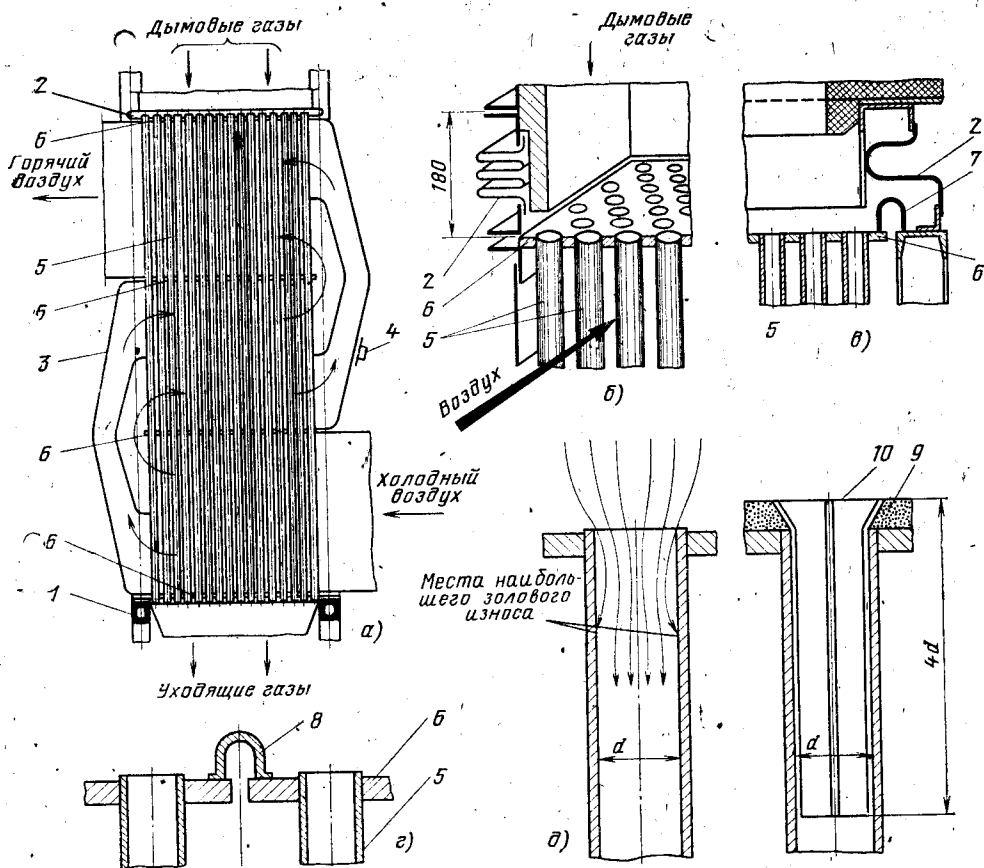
Конструкция стального однопоточного и трехходового по воздуху трубчатого воздухоподогревателя:
